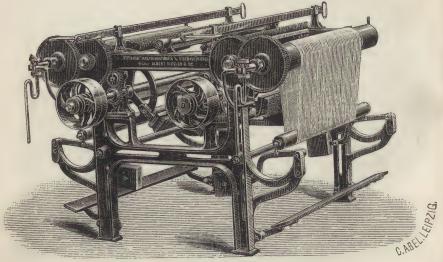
Garn=, Burft= und Blang= refp. Schlichtmaschinen.
